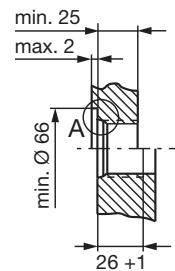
Wegaufnehmer BTL5...H/W..., Maßzeichnung
